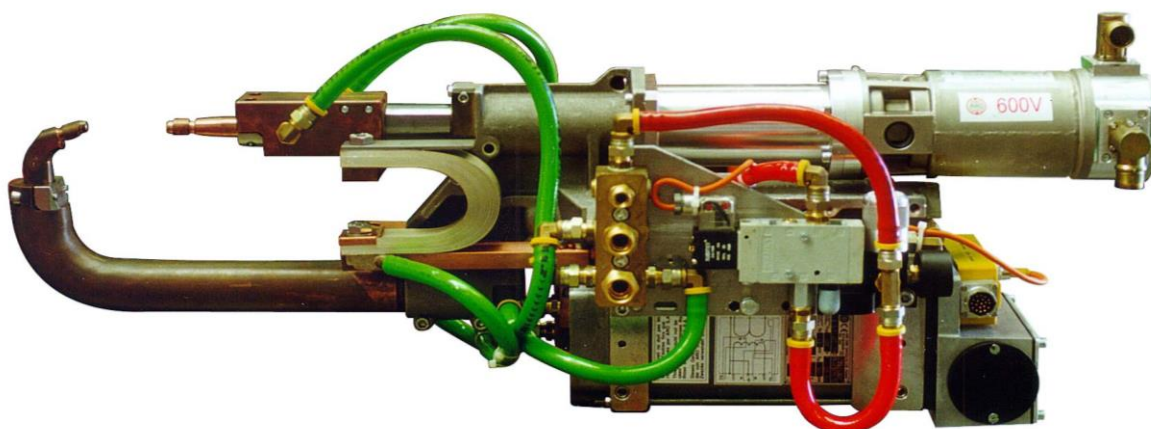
Pistola de solda por ponto de resistência. Fonte: TWI
